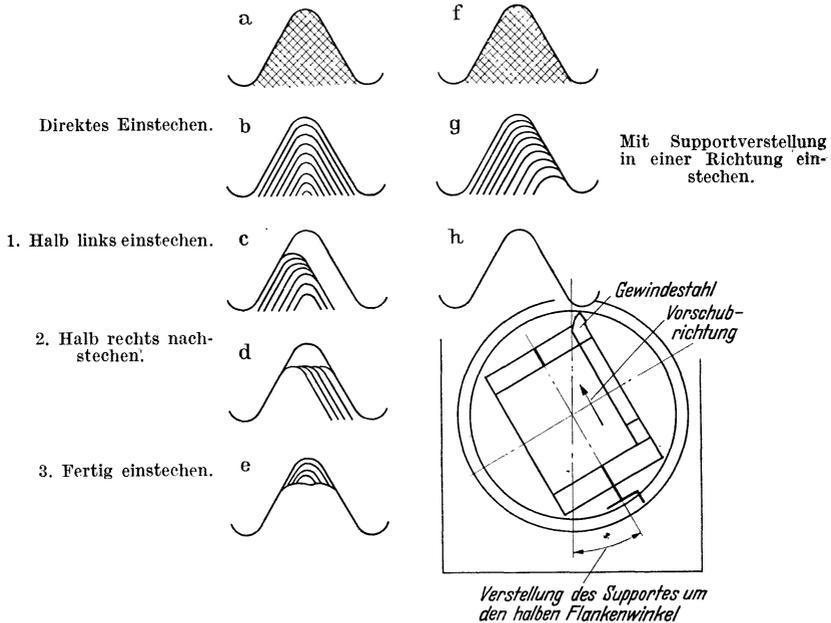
Verschiedene Einstechverfahren beim Gewindedrehen.
